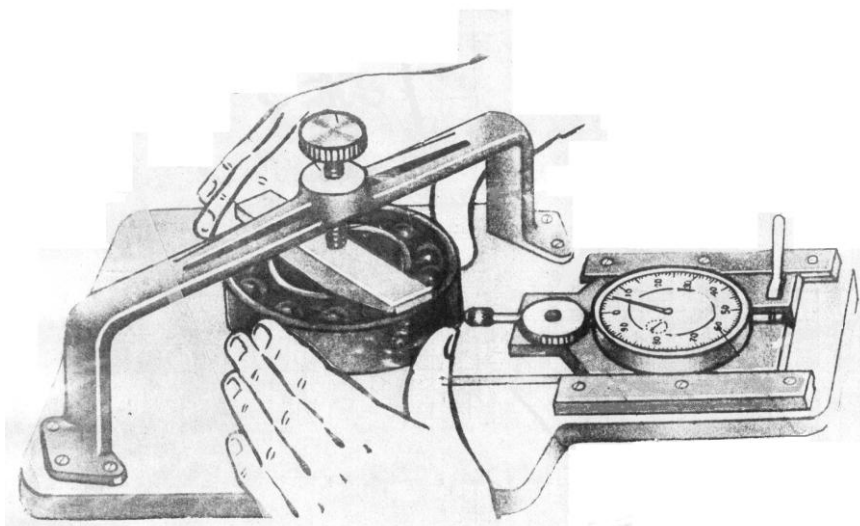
Схема измерения радиального зазора подшипника качения на приборе КИ-1223.
